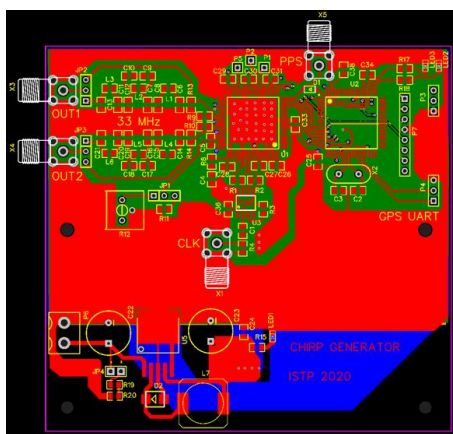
Разводка печатной платы миниатюрного ЛЧМ КВ-передатчика
